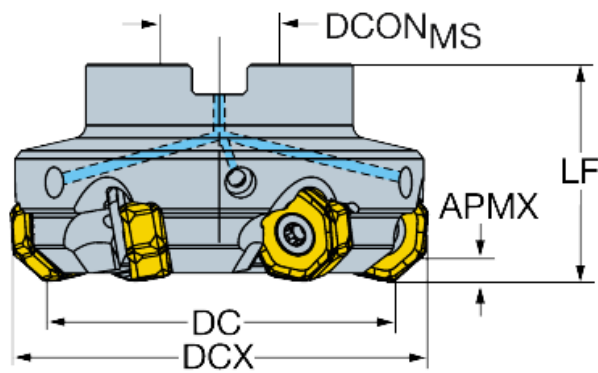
Торцева фреза CoroMill® A745-076R25-21H
